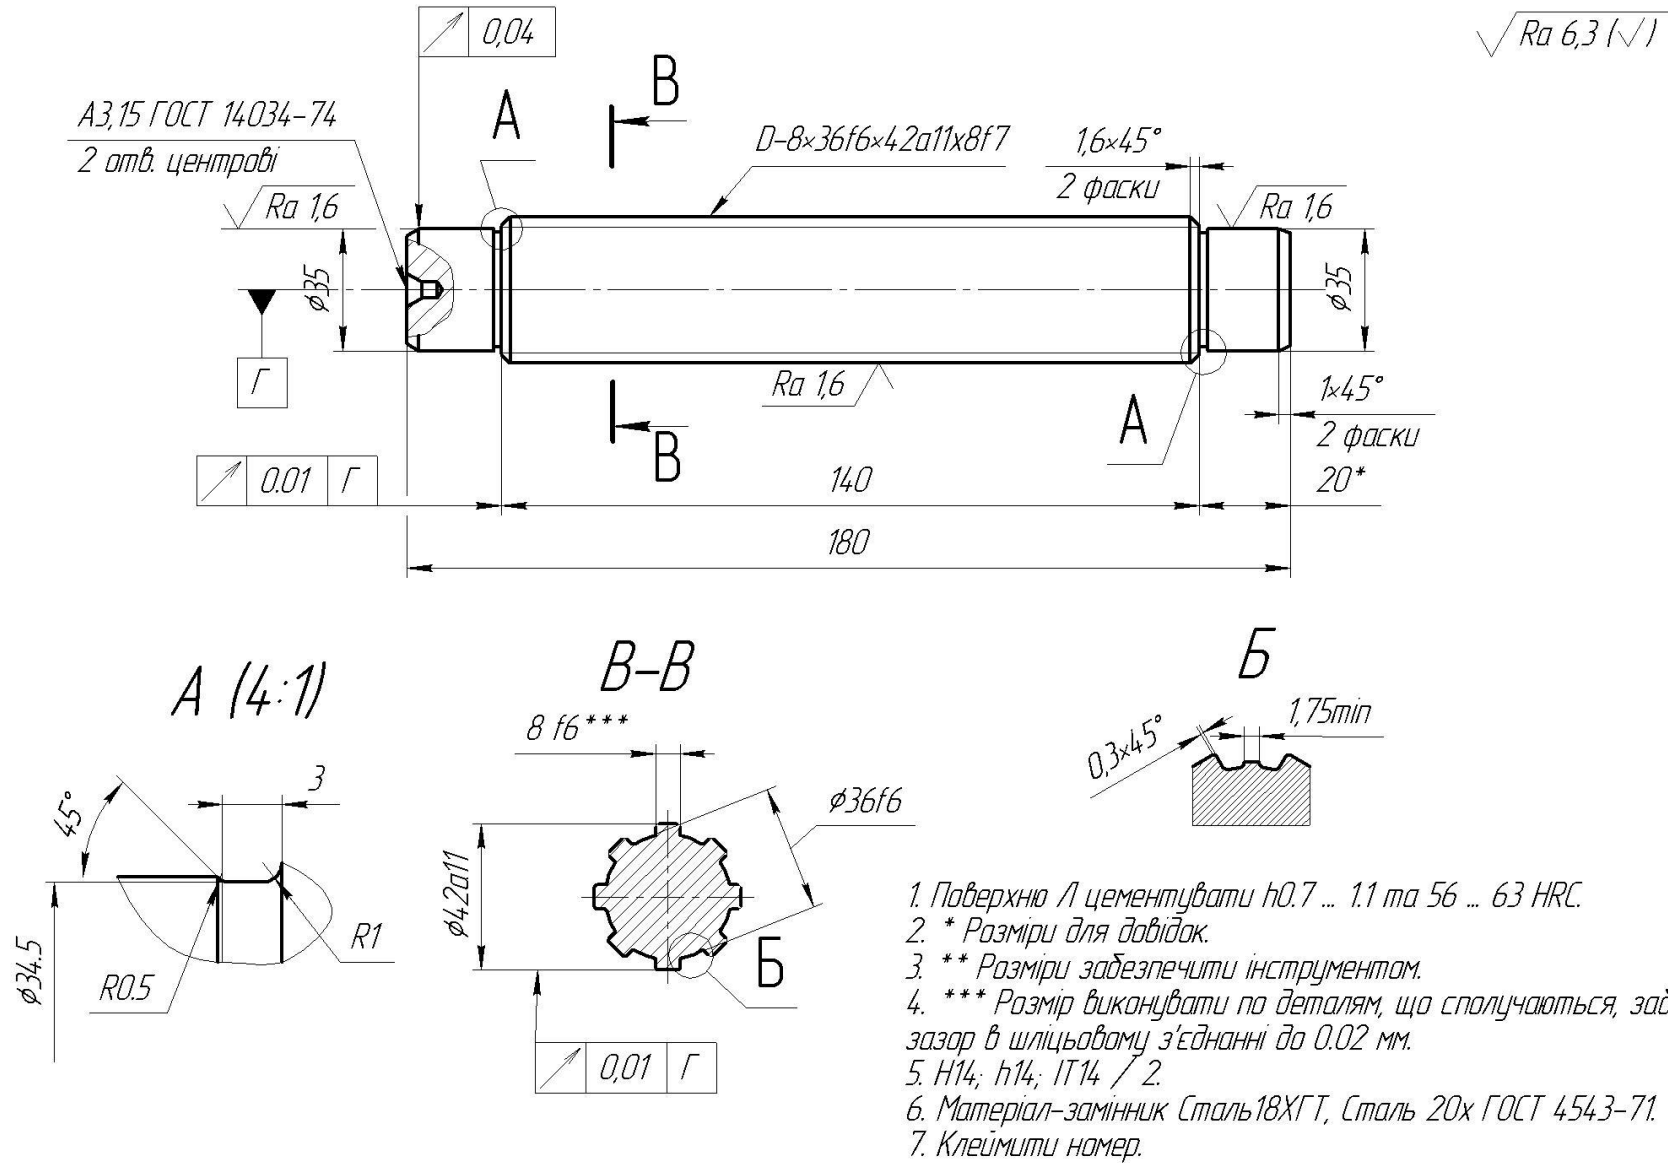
Кресленик деталі «Вал шліцьовий»
